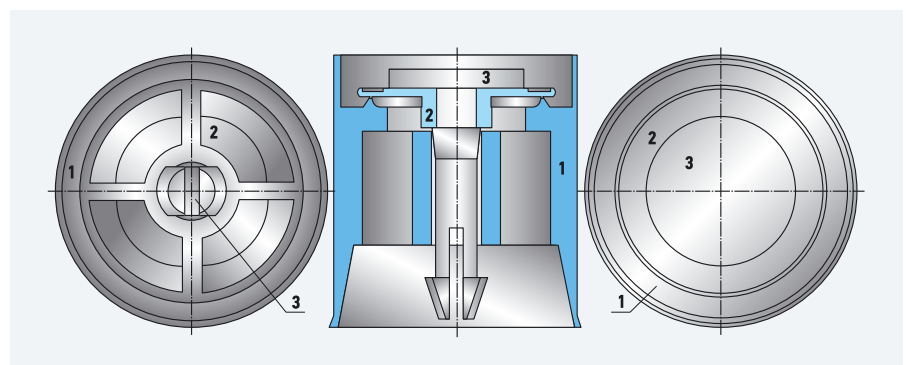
Конструктивная схема улучшенного обратного клапана фирмы «ИнкоЭр» (1 — корпус; 2 — уплотнение; 3 — шток)
